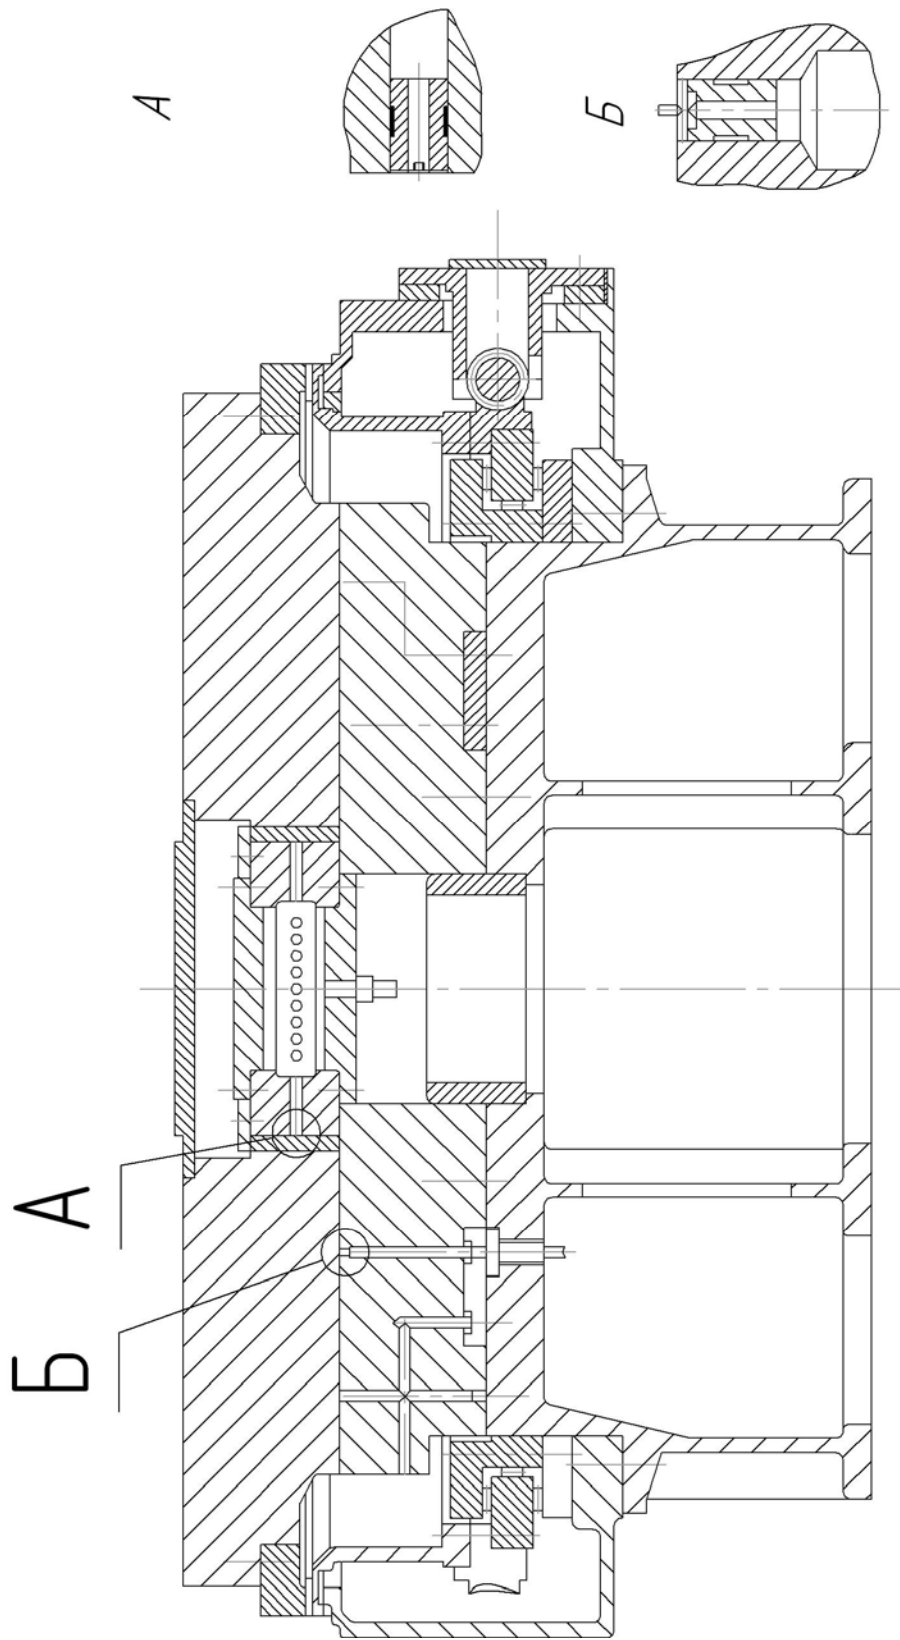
Аэроэстатические направляющие алмазно-фрезерного станка
